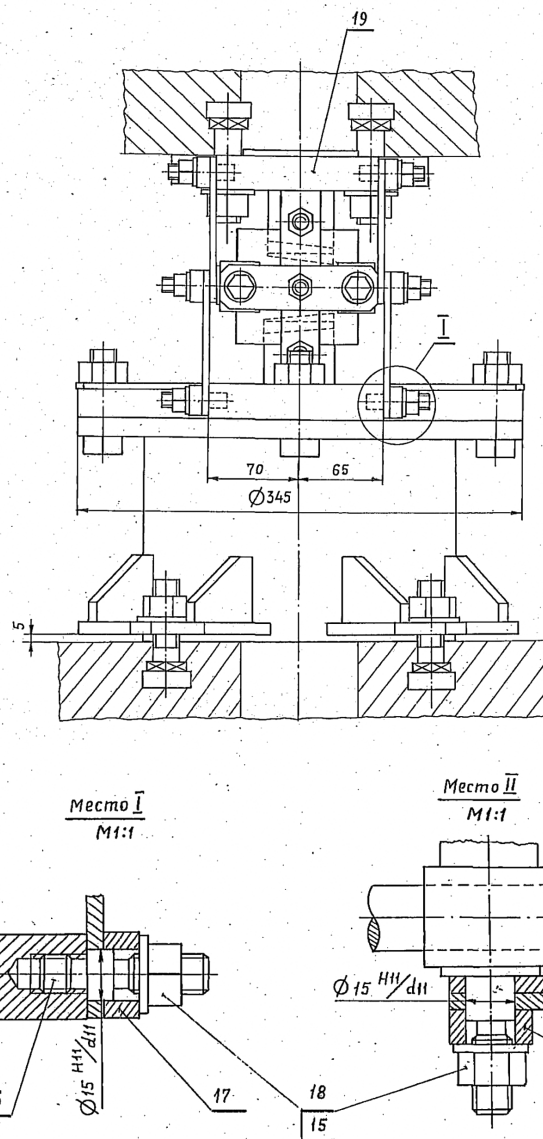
Модернизированная конструкция лабораторного устройства с привязкой к гидравлическому прессу:
